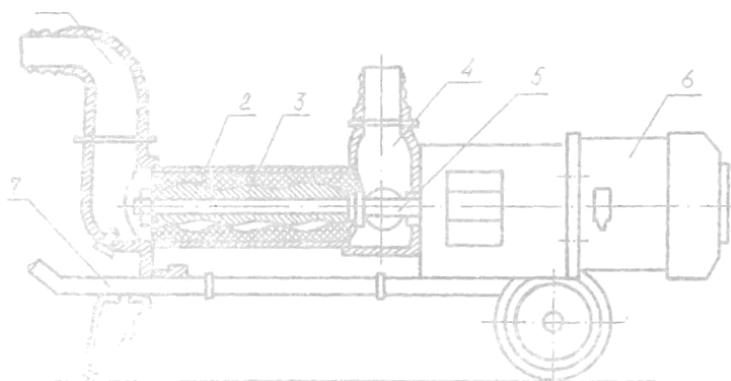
Schema pompei cu șurub: 1-racord de aspirație; 2-stator din cauciuc; 3-rotor elicoidal metalic; 4-racord de refulare; 5-arbore; 6-motor electric; 7-cărucior.
